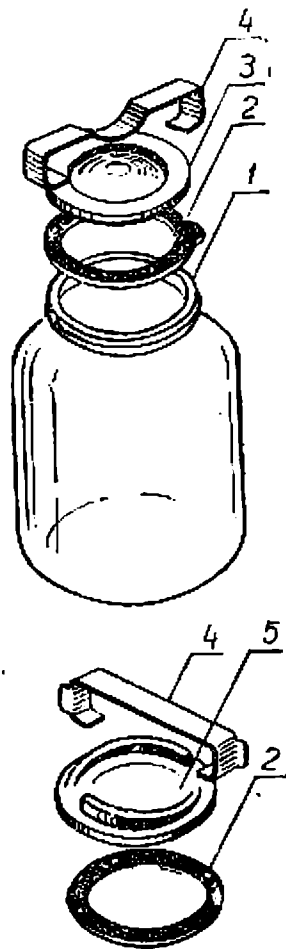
Банка с крышками из нержавеющей стали и стекла:
